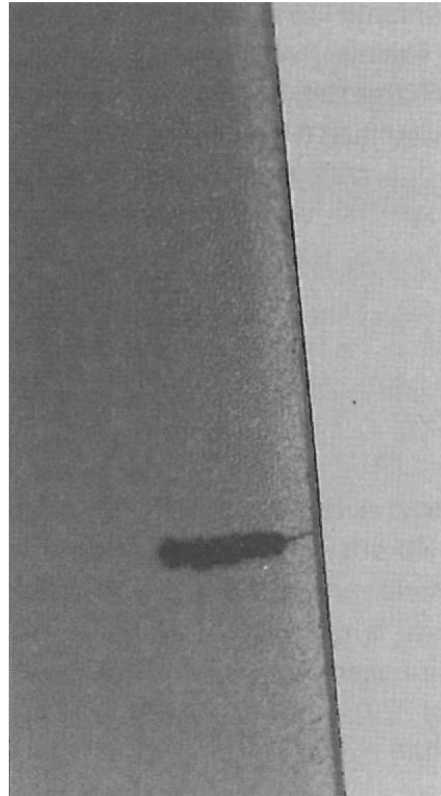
Cara de presión del álabe que se muestra en la Figura 6-15. Desde este punto de vista la grieta se puede ver con líquidos penetrantes.
